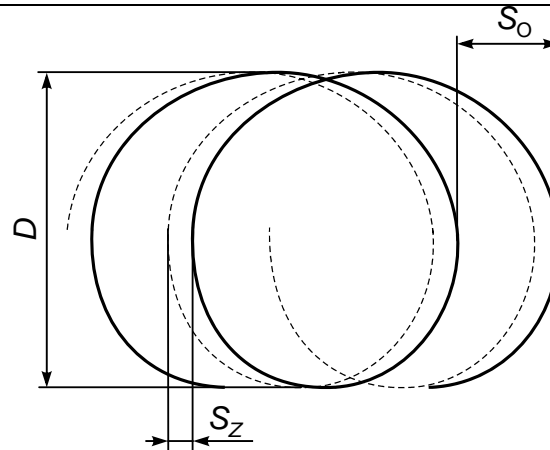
Траектории рабочих движений двух смежных зубьев осевой цилиндрической фрезы (для $z = 4$, $S_0 = 0,32D$)
